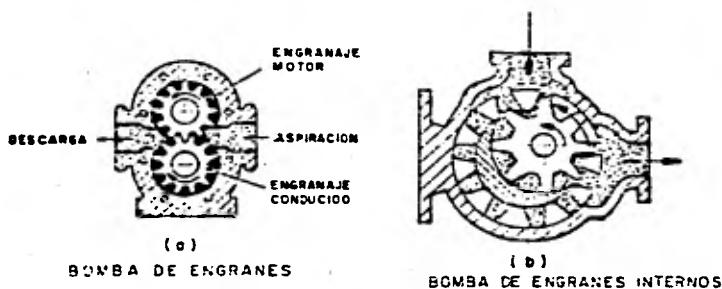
BOMBA DE ENGRANAJES.
